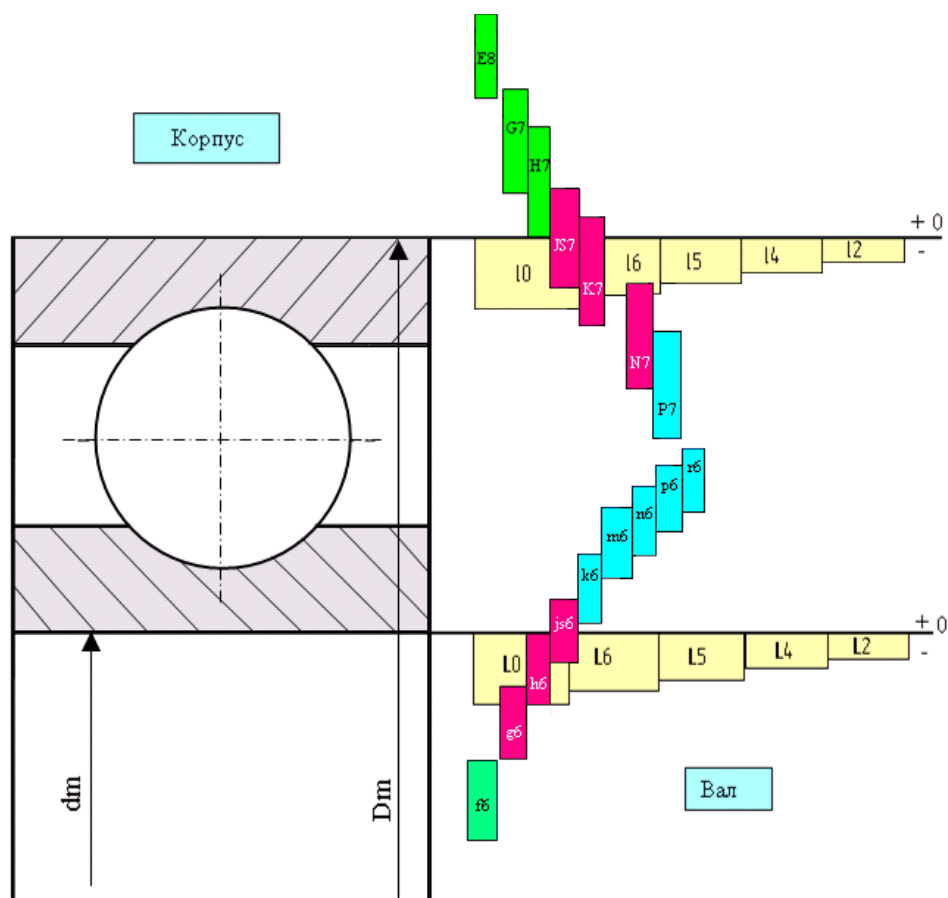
Схема расположения полей допусков для подшипников качения (выборочно)
